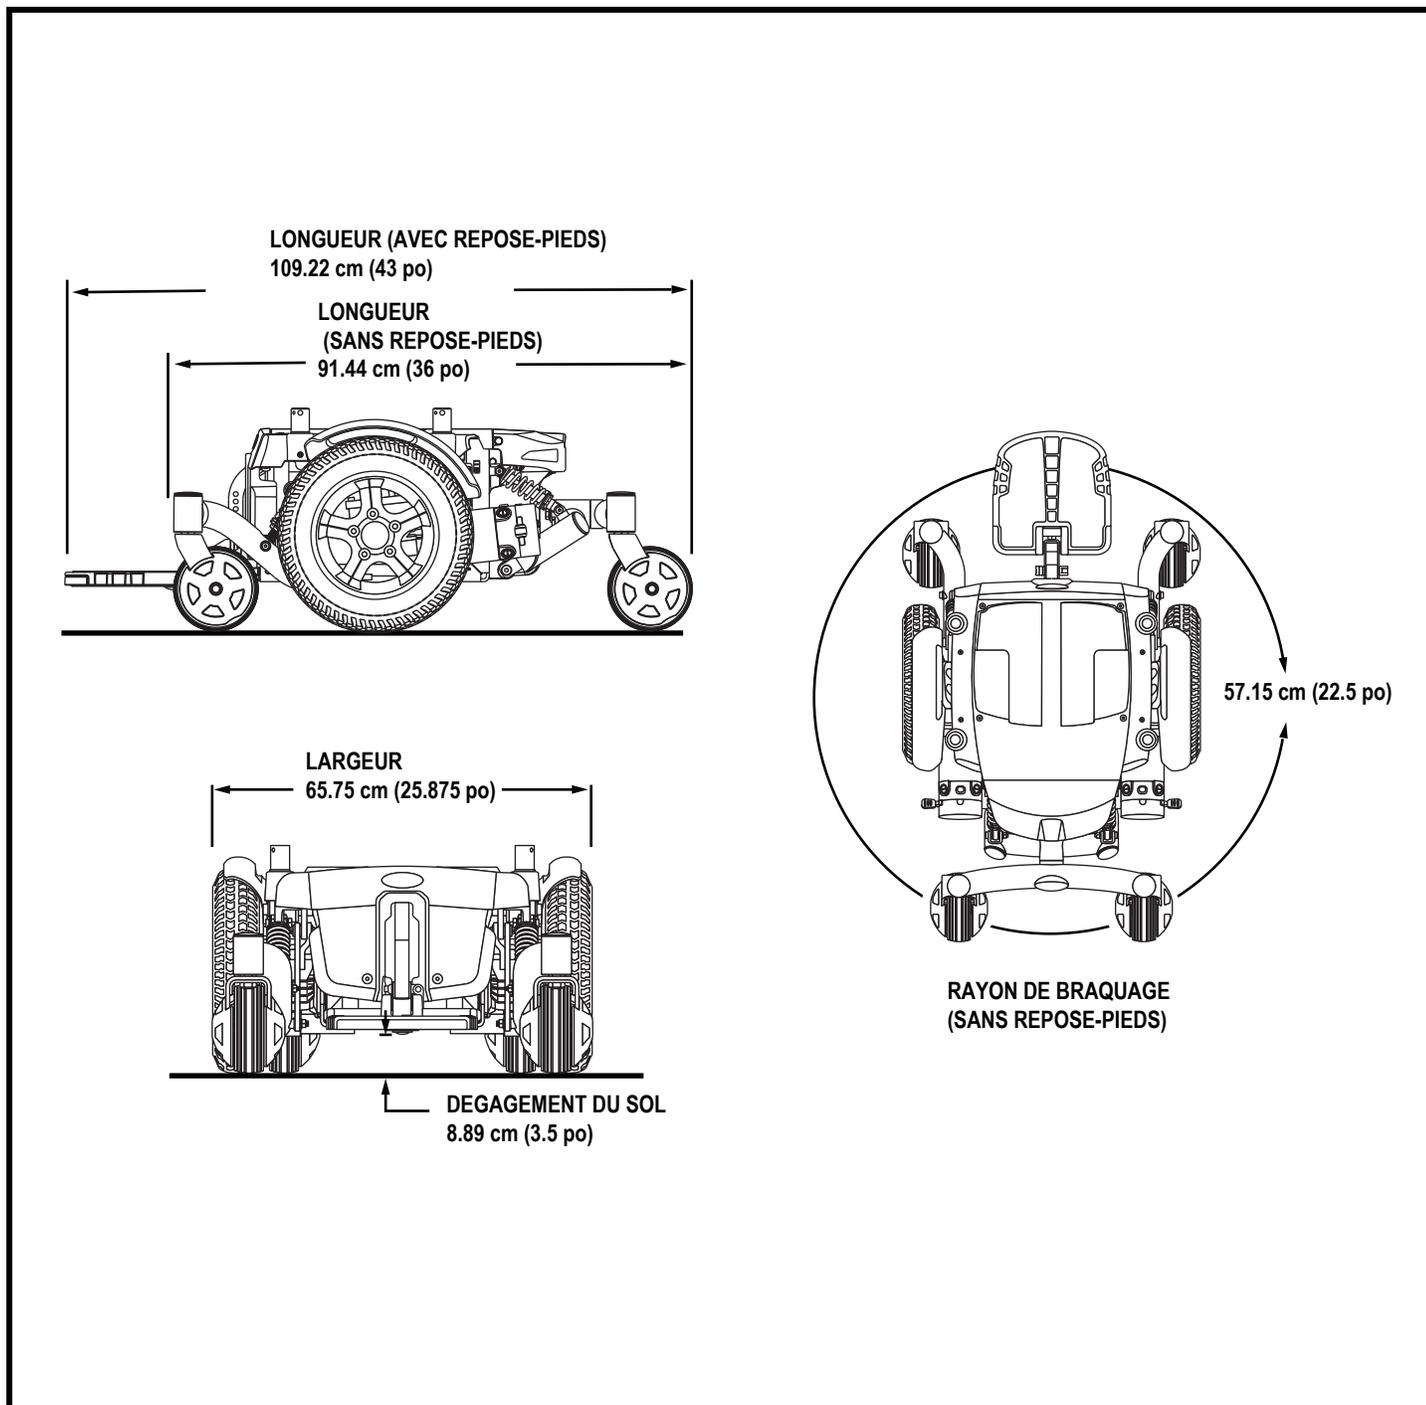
Quantum 6000Z dimensions et dégagement au sol
